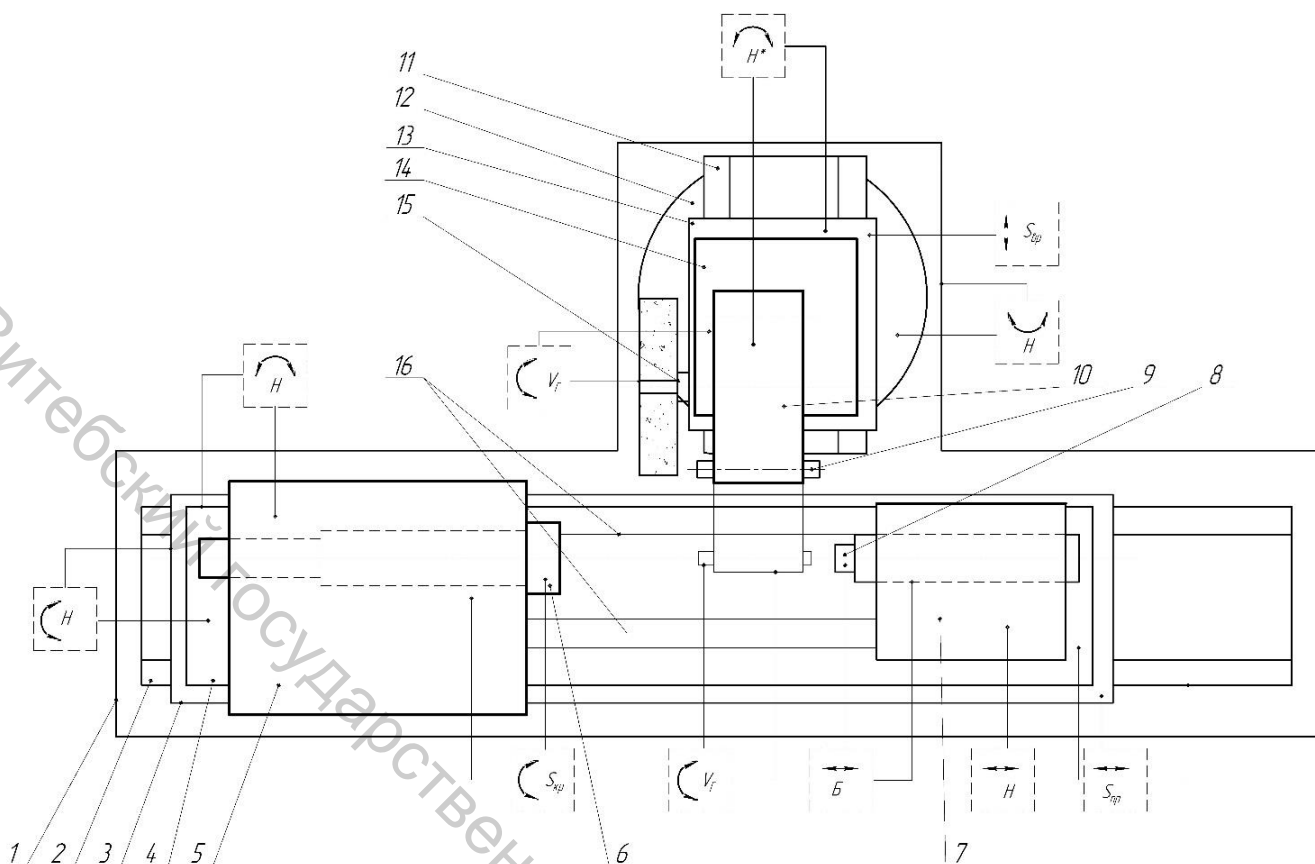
Схема компоновки и относительных движений узлов универсального круглошлифовального станка: 1 – станина; 2 – продольные направляющие станины; 3 – продольная каретка; 4 – стол; 5 – передняя бабка (изделия); 6 – шпиндель изделия (заготовки); 7 – задняя бабка; 8 – пиноль задней бабки; 9 – внутришлифовальный шпиндель; 10 – внутришлифовальная бабка (поворотная); 11 – поперечные салазки; 12 – поворотный стол; 13 – поперечная каретка; 14 – шлифовальная бабка; 15 – шлифовальный шпиндель; 16 – направляющие стола; H – наладочное относительное движение; H\* – то же в вертикальной плоскости; Б – базисуемое движение, остальные движения – рабочие
